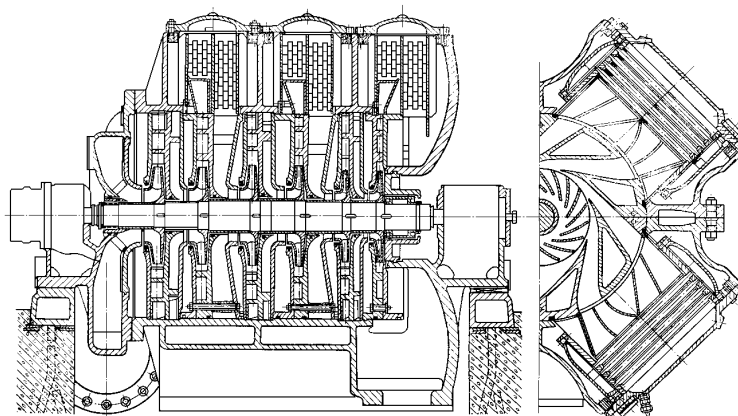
Четырёхступенчатый центробежный компрессор
